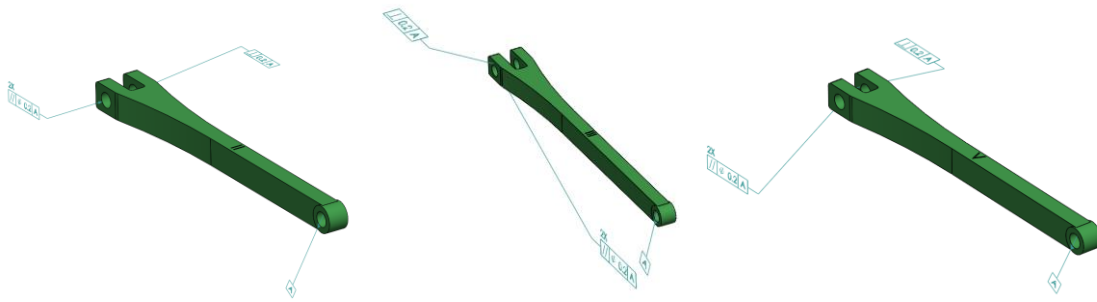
Tolerancias geométricas "Barra 3" dedos
